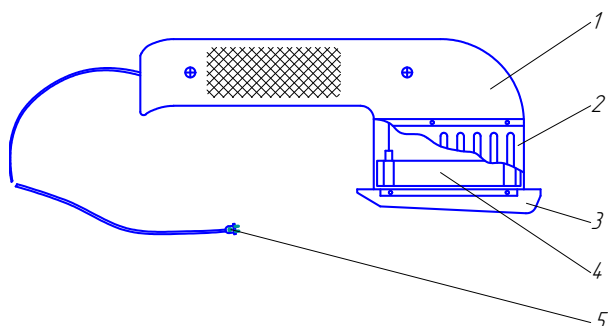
Устройство для сварки пленок косвенным нагревом ПСП-40:
